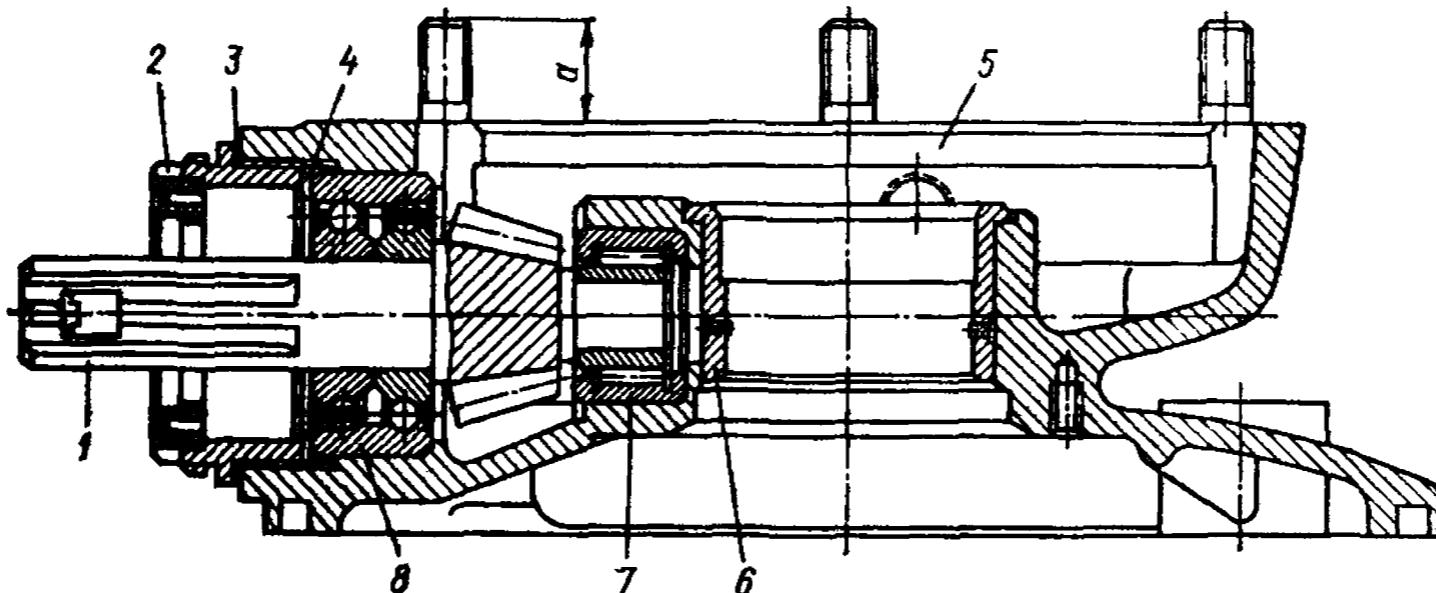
Картер главной передачи с ведущим зубчатым колесом в сборе:
